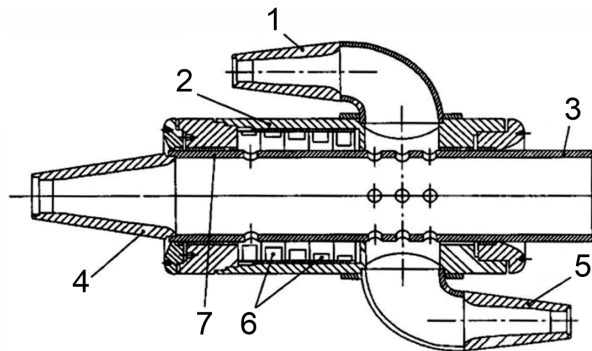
Гідромоніторна головка: 1 – відбійна насадка; 2 – корпус, що обертається; 3 – ствол; 4 – врубова насадка; 5 – транспортуюча насадка; 6 – гальмо; 7 – підшипник
